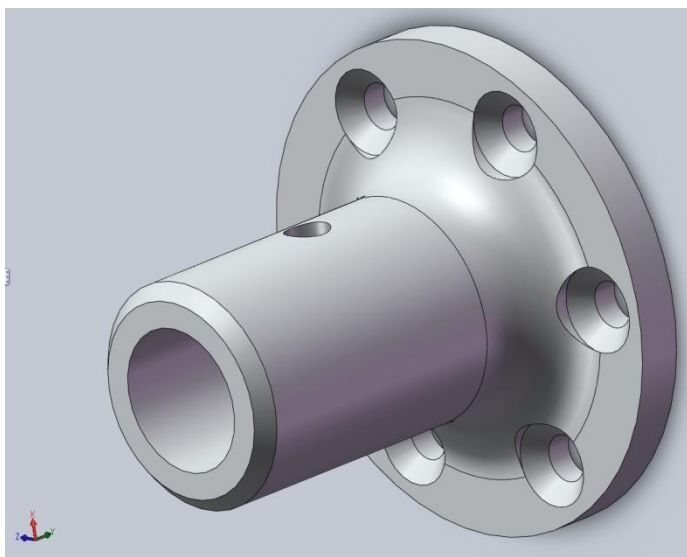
Desenho CAD Final do Adaptador Motor-Veio
